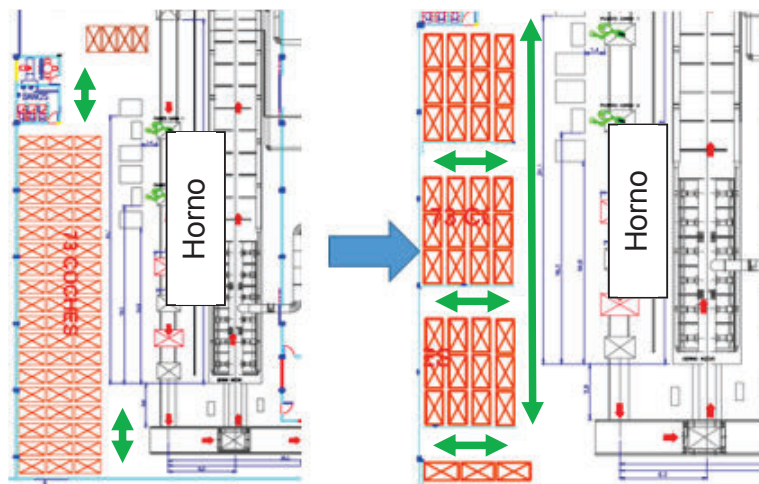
Propuesta de diseño de parqueadero para zona de horno izquierdo
